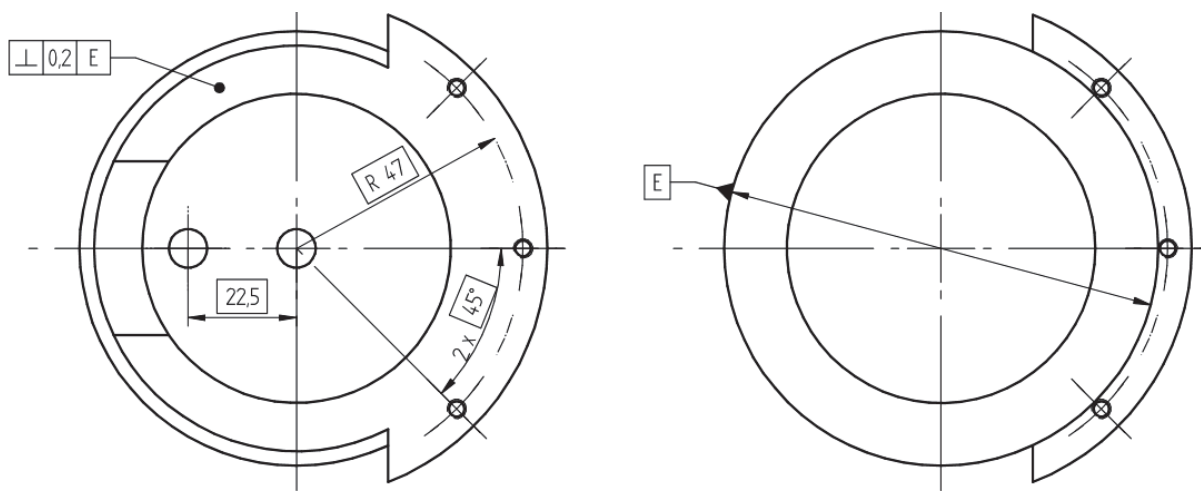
Umístění prvků s pevnými tolerancemi pro součást "otočný stůl"
